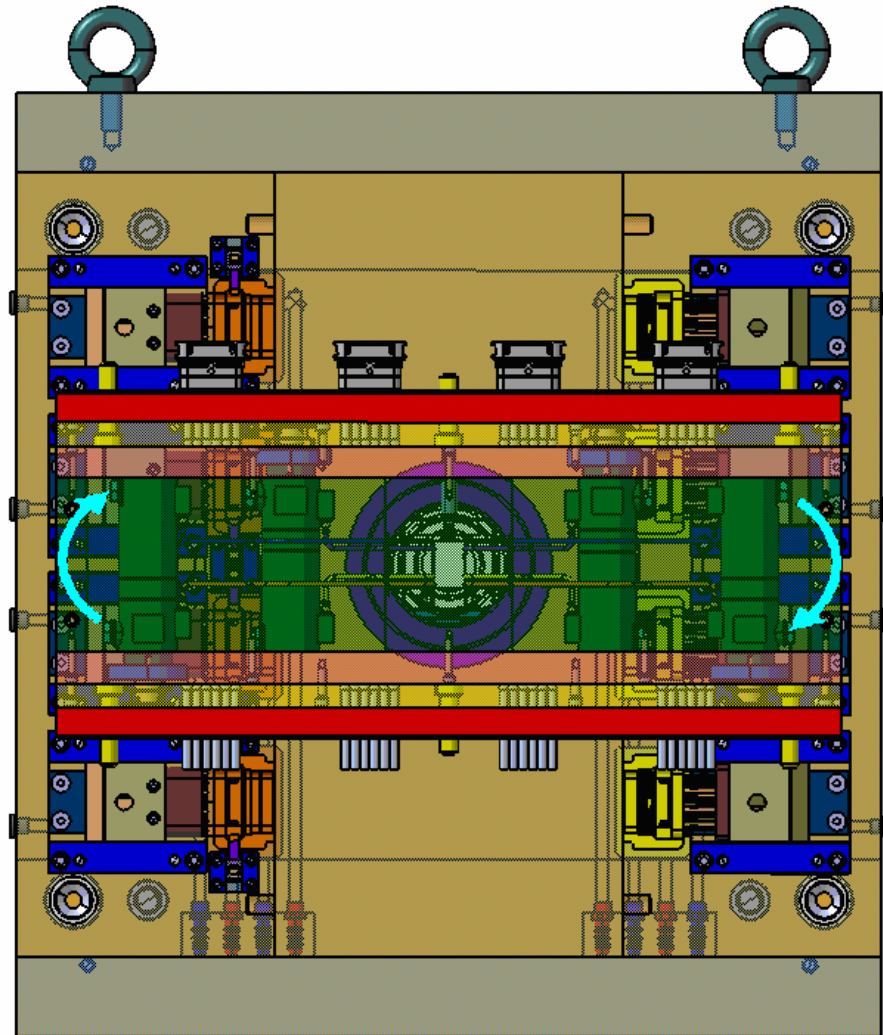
Zobrazení vysunutí stírací desky vyhazovacího systému
